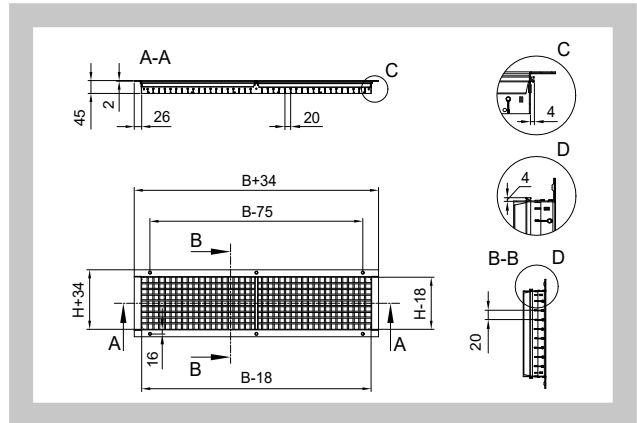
Einstellbare Lamellen vertikal - zweireihig
